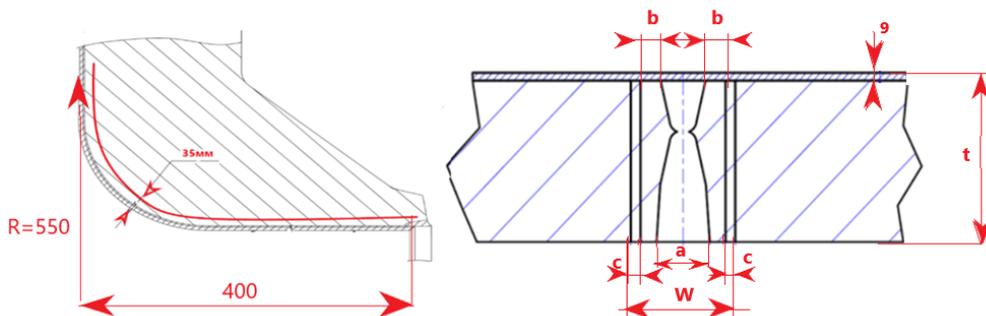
Зона контроля сварных соединений корпуса реактора и радиусных переходов
